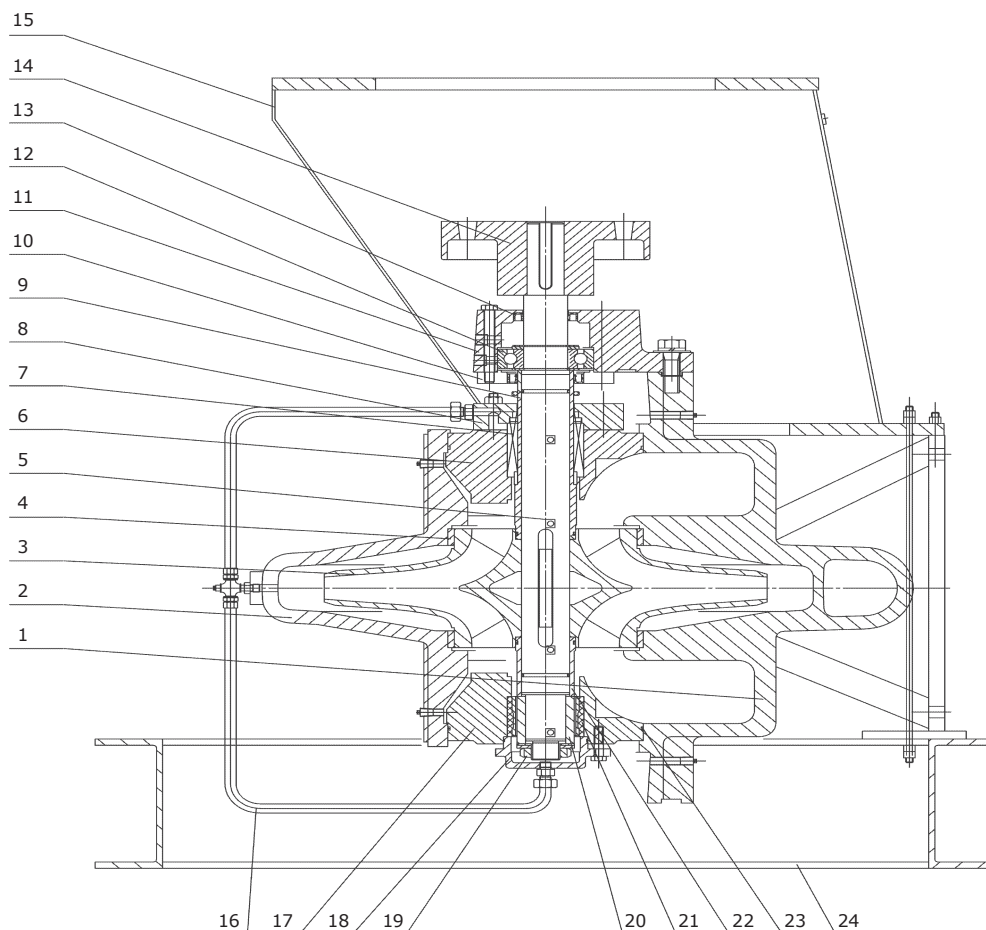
Вид в разрезе, стандартный тип исполнения 4
